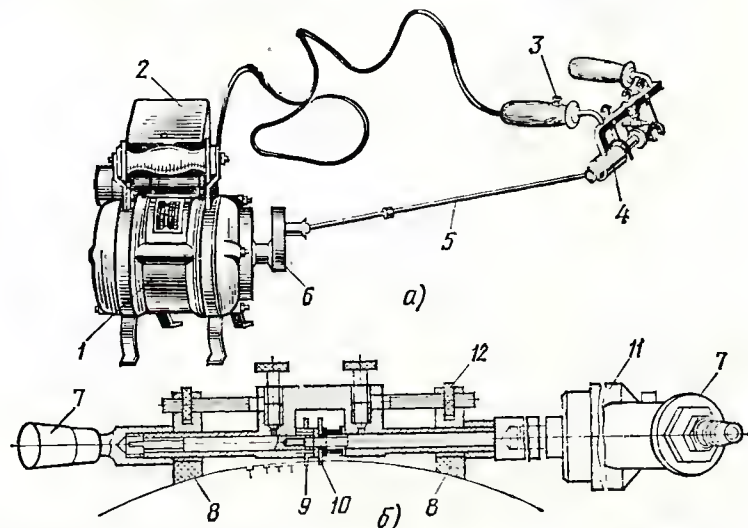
Переносные устройства для продорозивания коллекторов с приводом от электродвигателя (а) и с пневматическим приводом (б): 1 — электродвигатель, 2 — магнитный пускатель, 3 — кнопка, 4 — рабочая часть, 5 — карданный вал, 6 — редуктор, 7 — рукоятка, 8 — упоры, 9 — направляющий диск, 10 — фреза, 11 — пневматическая сверлильная машина, 12 — гайка
